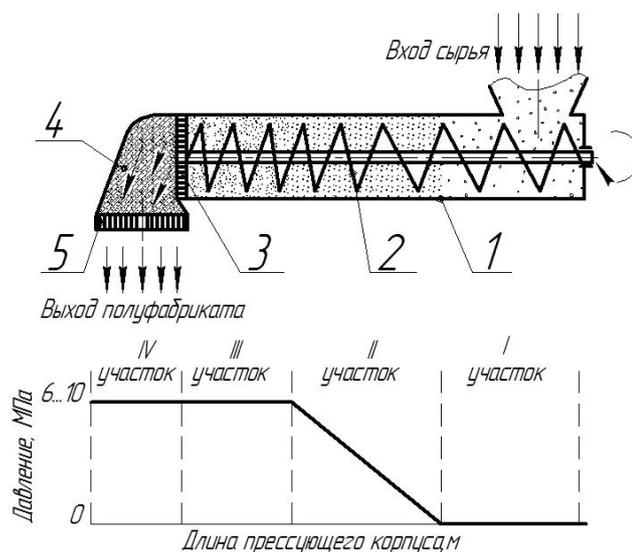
Схема прессующего корпуса макаронного пресса: 1 – корпус; 2 – шнек; 3 – перфорированная решетка; 4 – предматричная камера; 5 – матрица
